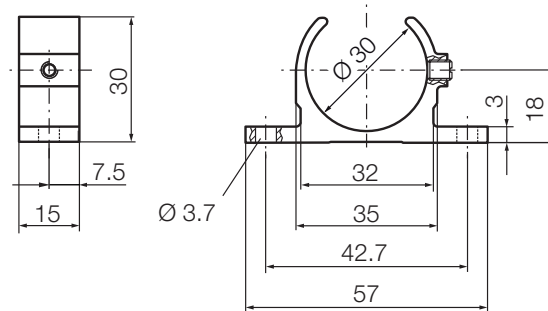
Befestigungsklammer BTL6-A-MF01-A-43
